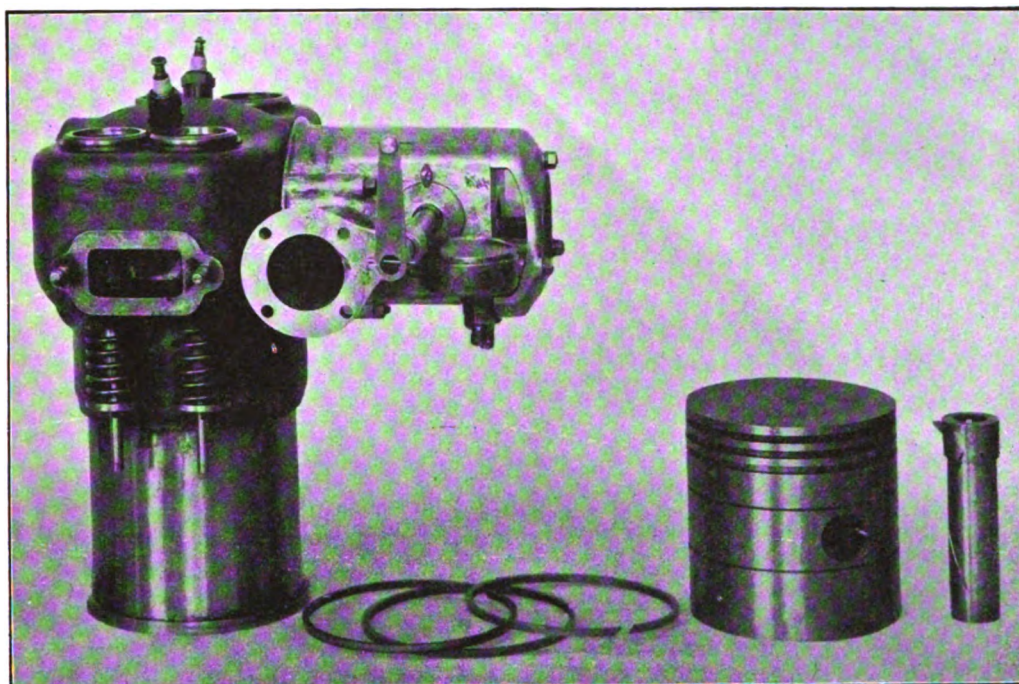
Zylinder mit Vergaser sowie kompletter Kolben des Maybach-Motors.
